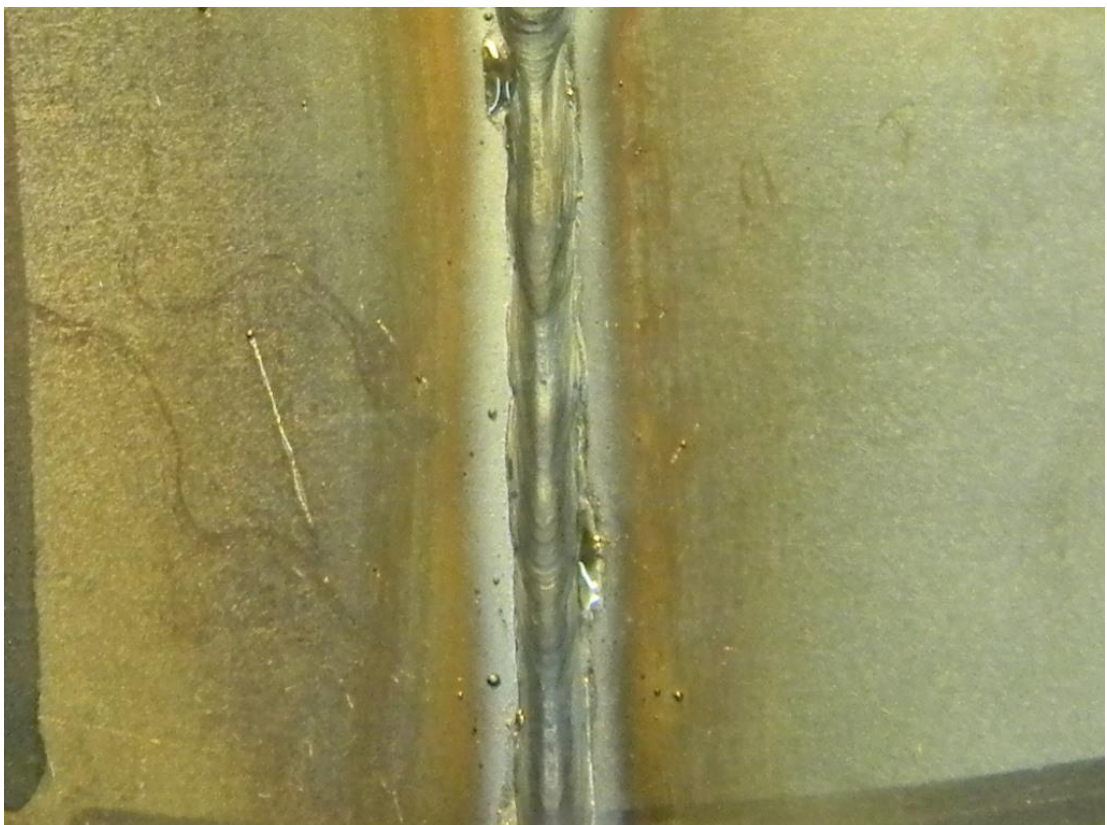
Образец после сварки подготовленный вырубкой контрольная без очистки вид снизу
